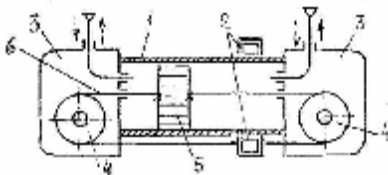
Схема бесштокового пневмоцилиндра:
